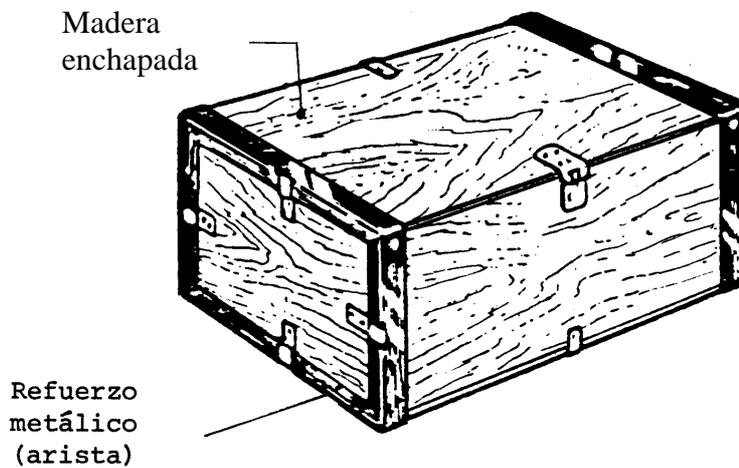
a) - Caja de madera enchapada, refuerzo metálico de las aristas
